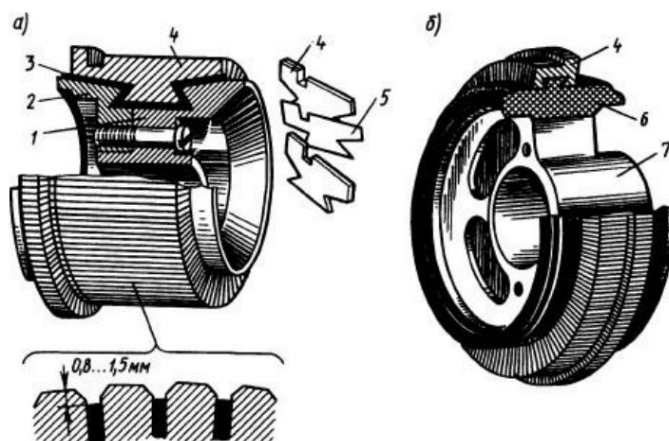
Устройство коллектора машины постоянного тока с металлическим (а) и пластмассовым (б) корпусом: 1 – корпус; 2 – нажимной фланец; 3 – изоляционные манжеты; 4 – коллекторные пластины; 5 – изоляционные прокладки; 6 – пластмасса; 7 – втулка
